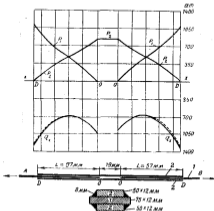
Кривые напряжений, получаемые при испытании фланцевых сварных швов.
